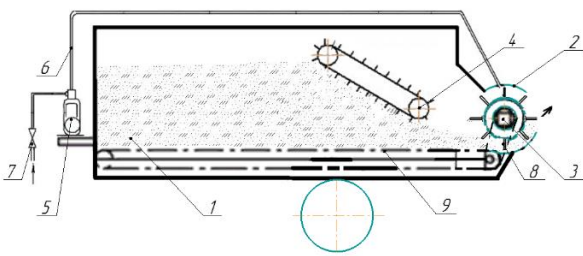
Схема удосконаленого подрібнювача та розкидача гною: 1 – кузов; 2 – корпус; 3 – лопатевий барабан; 4 – ущільнювальний транспортер; 5 – гнойовий насос; 6 – нагнітальний трубопровід; 7 – перемикач; 8 – лопатка, 9 – скреперний транспортер
